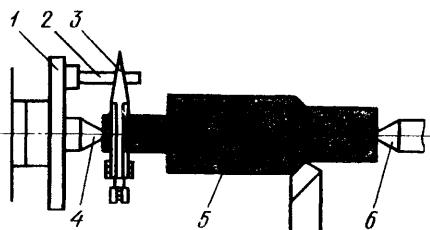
Обработка заготовки в центрах с приводом от поводкового патрона
